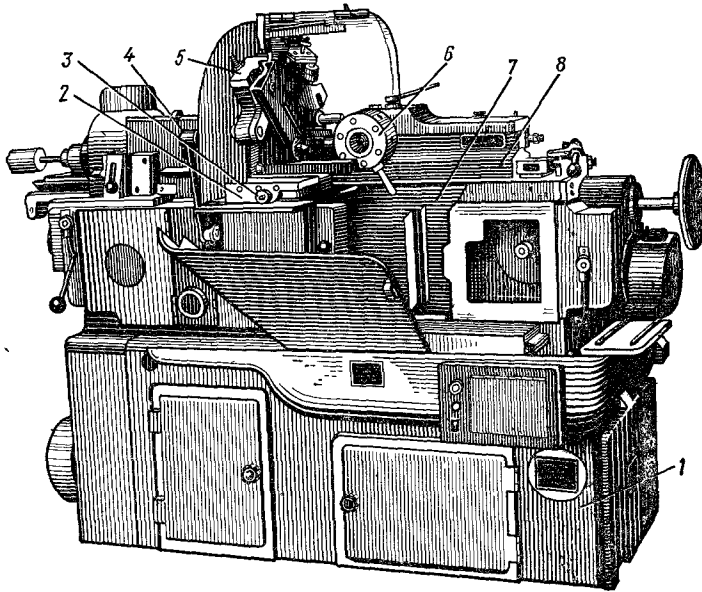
Токарно-револьверный автомат мод. 1Б140
